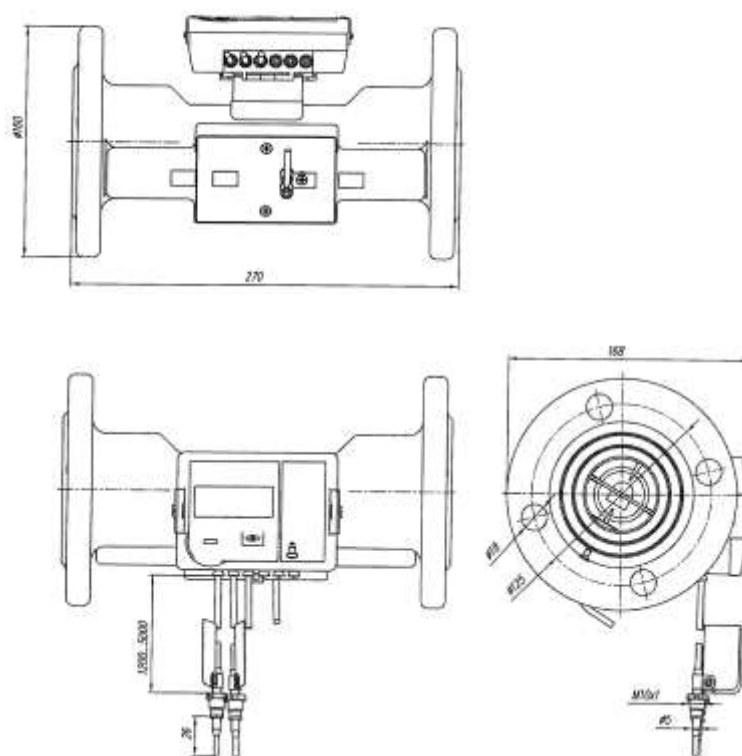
Присоединительный размер к трубопроводу DN50 , длина L= 270 мм
